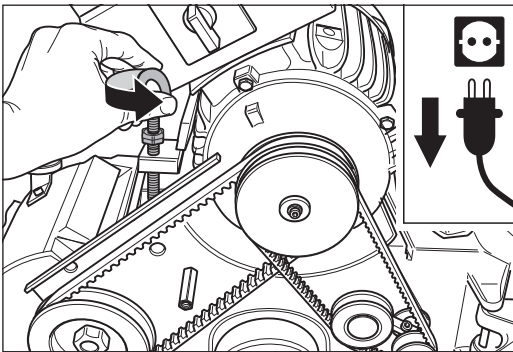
Die Ringschraube am Motor gegen den Uhrzeigersinn drehen.
